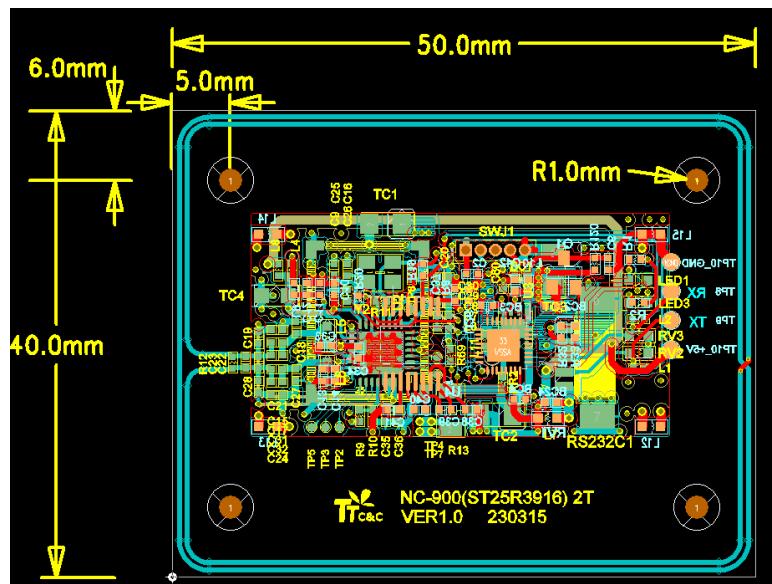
NC-900 CAD Drawing 50*40mm(+/-2mm)
